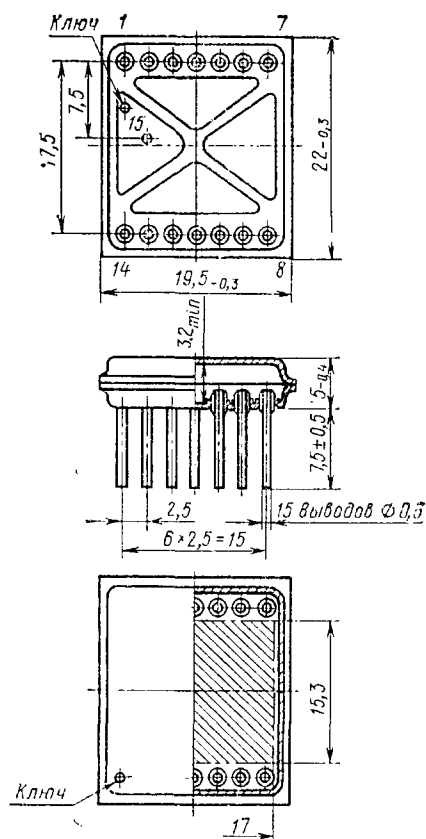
Конструкция металлостеклянного корпуса 1206 (153.15-1)
